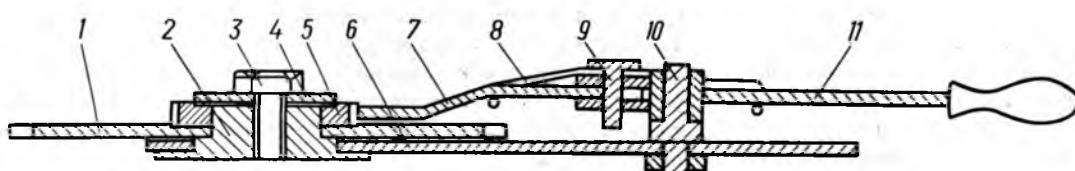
Приспособление для насечки зубьев на пильном диске:
